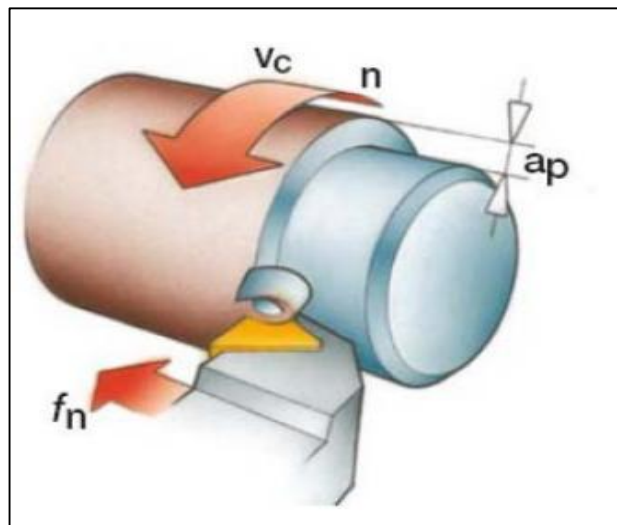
Illustration d'un procédé d'usinage (tournage) [2].
